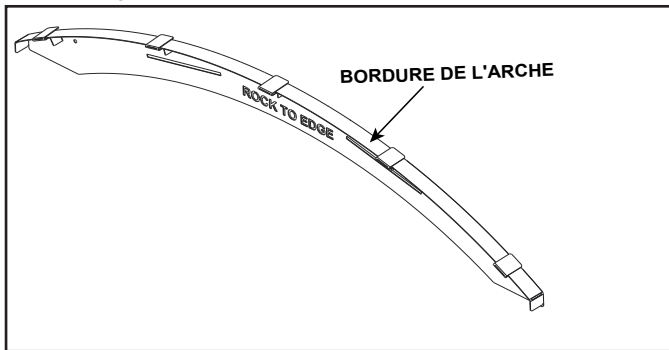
Pièces de finition du haut et de la voûte assemblées
